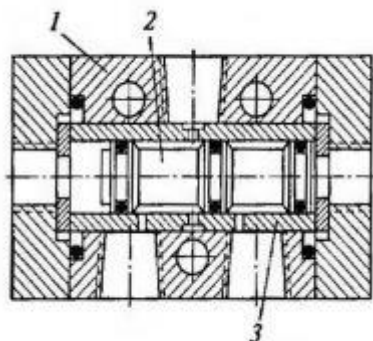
Пневматический золотниковый распределитель: 1 - корпус; 2 - золотник; 3 – гильза.
